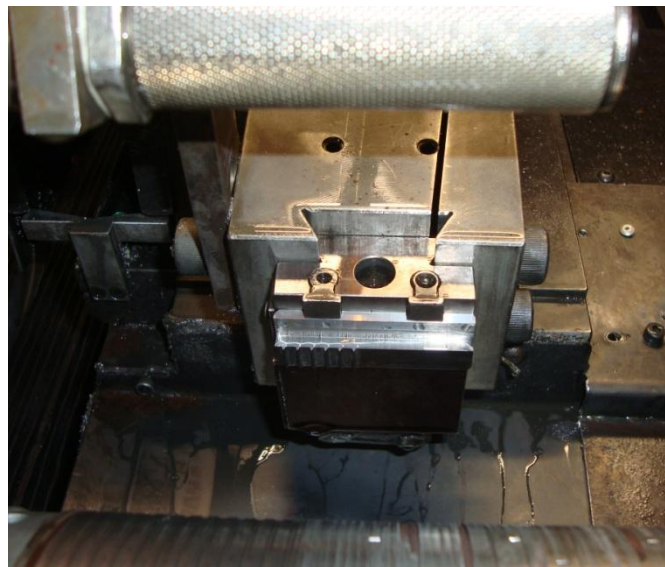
Montagem do conjunto porta-ferramenta e ferramenta no dispositivo do torno.
